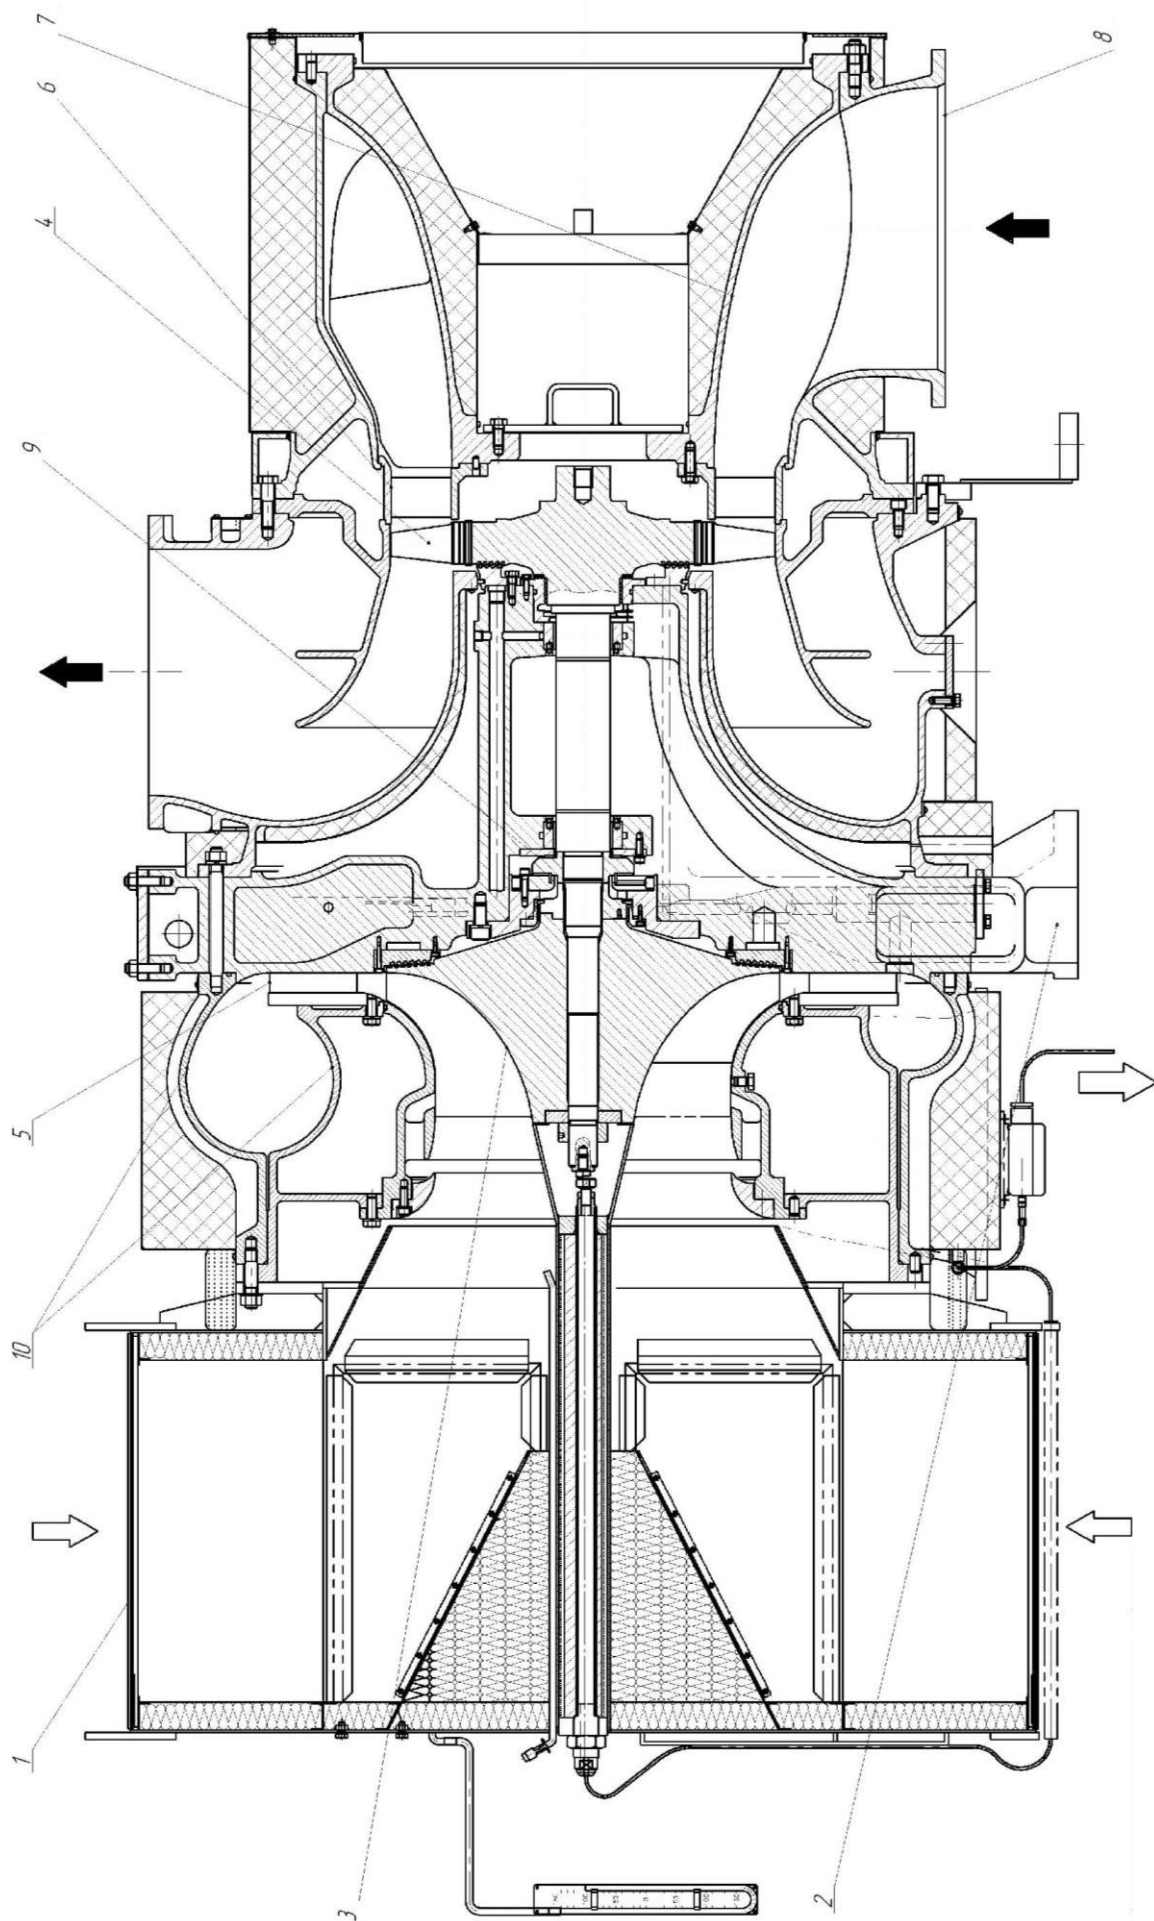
Турбіна суднового двигуна: 1 – глушник; 2 – корпус; 3 – турбінне колесо; 4 – лопатка; 5 - дифузор; 6 – насадка; 7 – впускний патрубок; 8 – впускний підшипник; 9 – упорний підшипник; 10 - спираль
